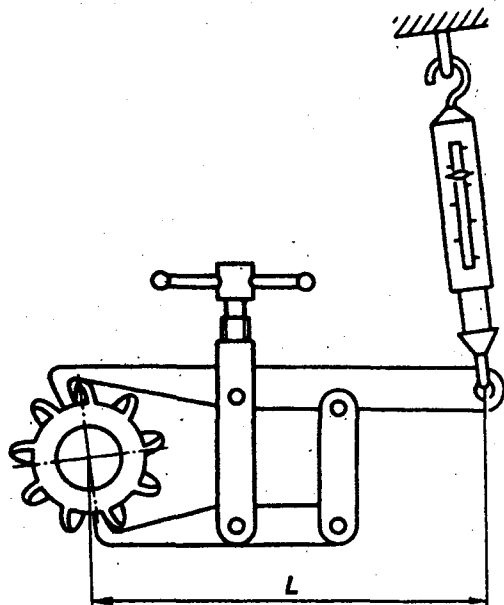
Динамометрическое приспособление (L — длина плеча, м)
